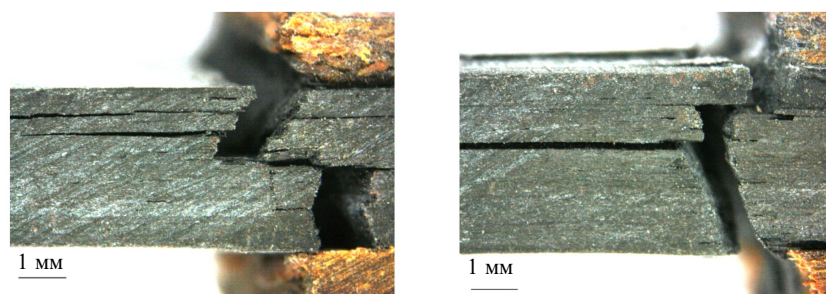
Вид разрушенных образцов из композита ЭЛУР-П с торца рабочей части: слева – образец №2; справа – образец №4 (по данным из [3])
